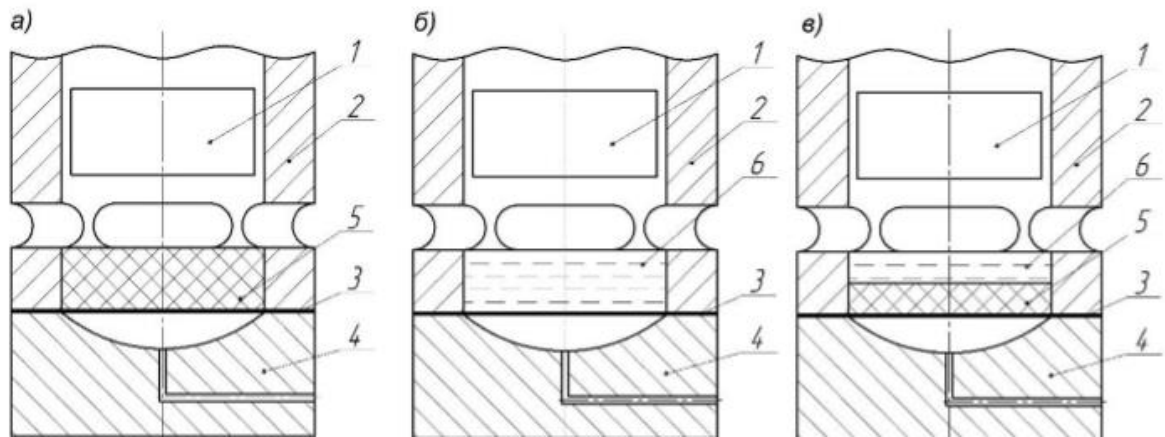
Схеми ударно-імпульсної витяжки рухомими середовищами: а – поліуретаном; б – рідиною; в – комбінована: 1 – бойок; 2 – стоббур; 3 – заготовка; 4 – матриця; 5 – рідина; 6 – еластичний блок (поліуретан)
